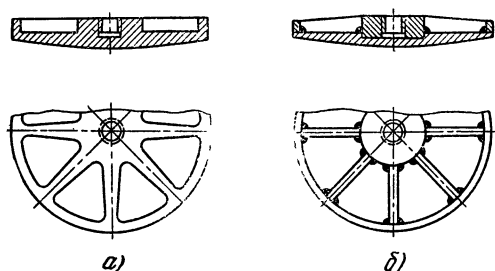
Облегченные металлические шлифовальники, а — из сплошного материала, б — сварной из стали.
